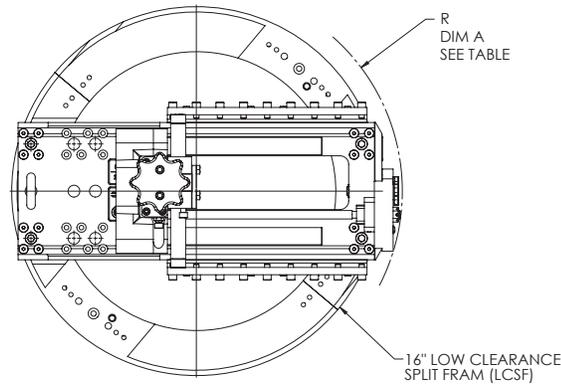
Innenbearbeitungs-Werkzeughalter (Artikelnummer. 60-708-00) und Werkzeug.
